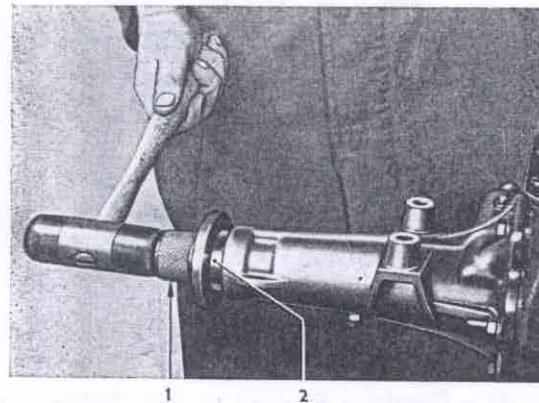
Doppellippendichtring in Getriebegehäuseverlängerung einschlagen
